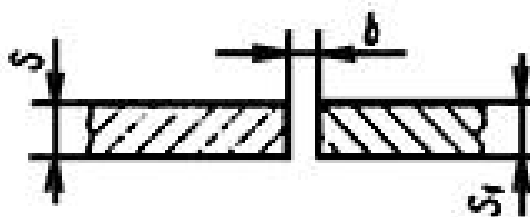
Конструктивный элемент подготовленных кромок свариваемых изделий С2 ГОСТ 14771-76 [25]
